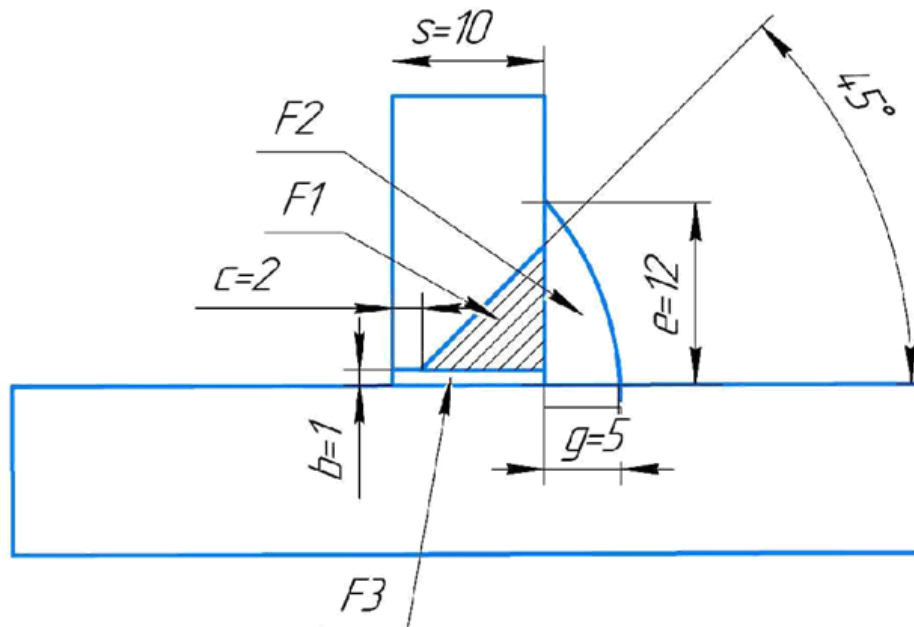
Схема площі наплавленого металу поперечного перерізу шва Т6
